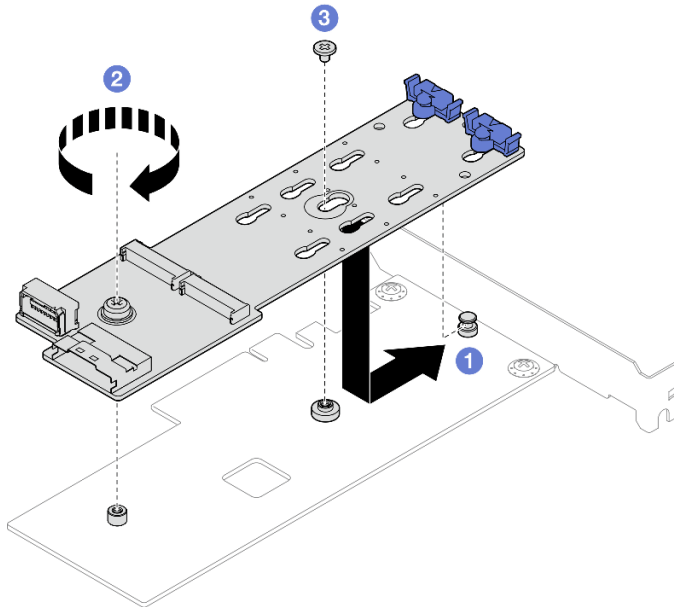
Befestigen des M.2-Bootadapters am PCIe-Adapter
